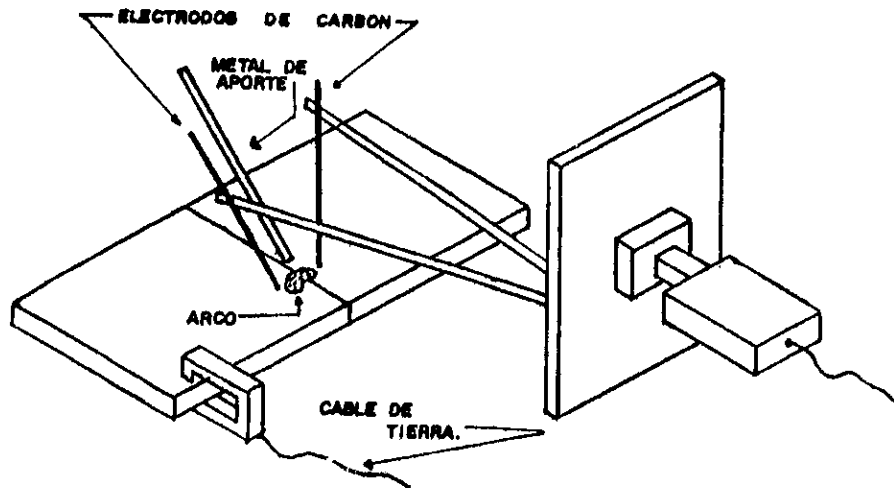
Soldadura de arco con carbones gemelos
